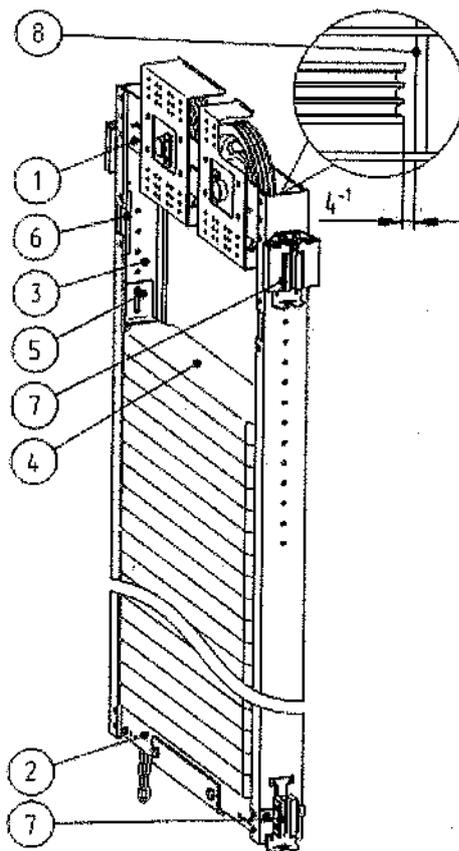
Противовес: 1 - Балка верхняя, 2 - балка нижняя, 3 - стойка, 4 - груз, 5 - прижим, 6 - планка, 7 - башмак, 8 - шпилька.
